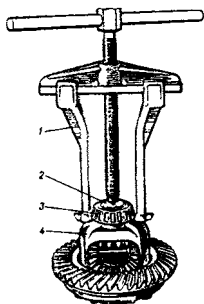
Снятие внутреннего кольца подшипника дифференциала
